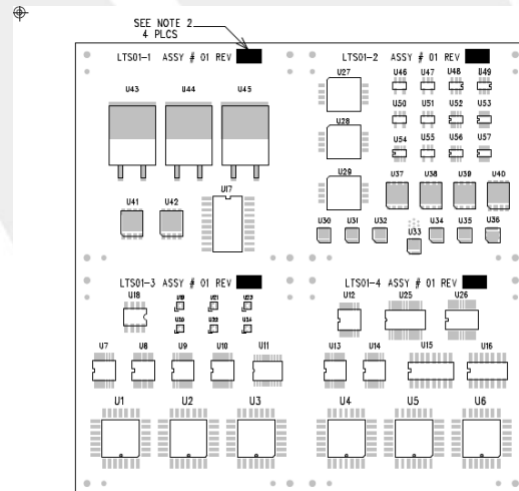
Diseño de placa de PCB utilizado para el proceso de montaje
